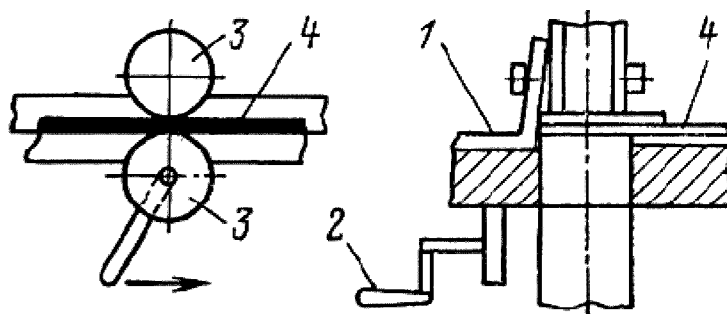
Эскиз установки для фальцевания: 1 — упор; 2 — рукоятка; 3 — валики; 4 — образец
